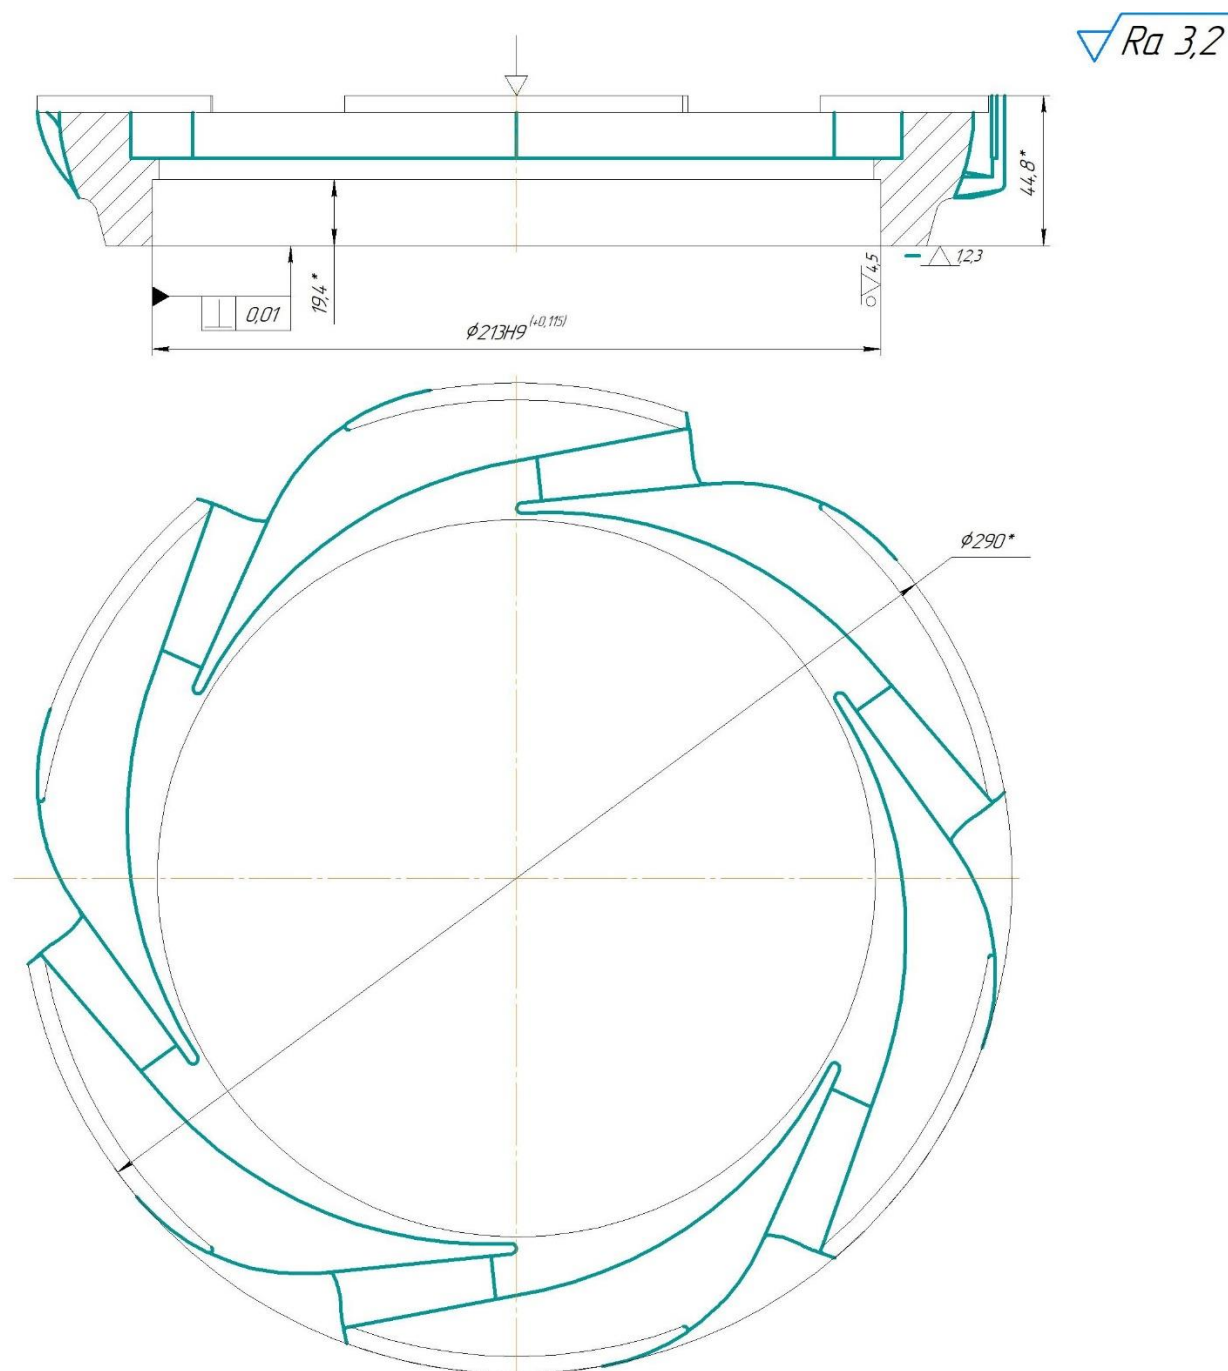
Операційний ескіз вертикально-фрезерної з ЧПК операції (варіант 2)
